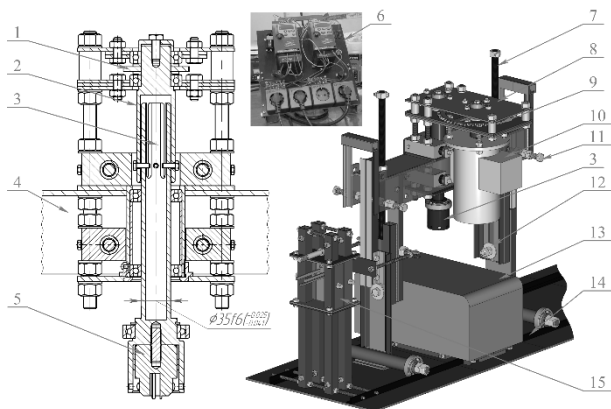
Машина трения: 1 – быстроходное колесо; 2 – быстроходный вал; 3 – державка образца; 4 – корпус каретки; 5 – сверлильный патрон для закрепления образца (схематично); 6 – блок управления; 7 – регулятор высоты (винтовая пара); 8 – мультипликатор; 9 – тихоходное колесо; 10 – фланцевый двигатель с лапами (схематично); 11 – фиксатор наклона (винтовая пара); 12 – ось наклона; 13 – плоскошлифовальный станок (схематично); 14 – угловой профиль (рельсы); 15 – регулируемый по высоте ползун с пневмопоршнем
